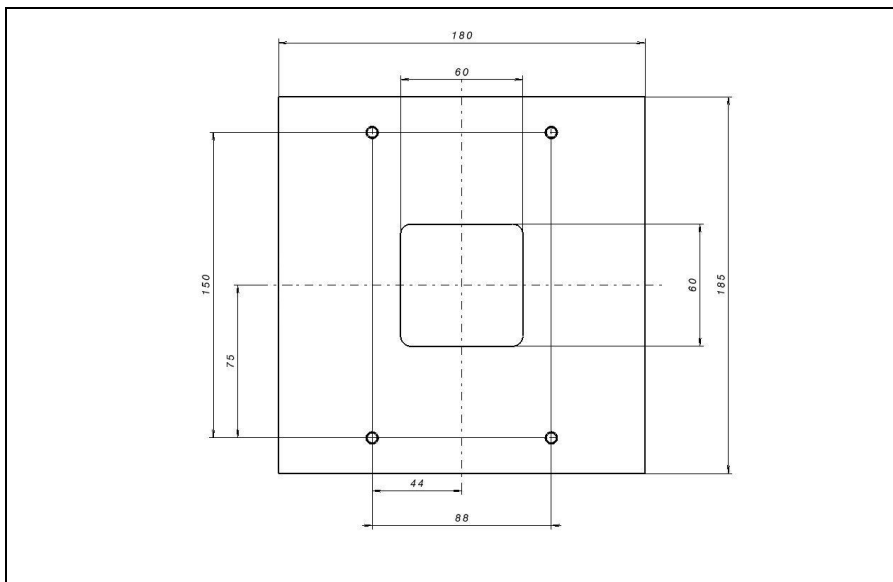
Bohrbild Standard-Adapterplatte BG D
